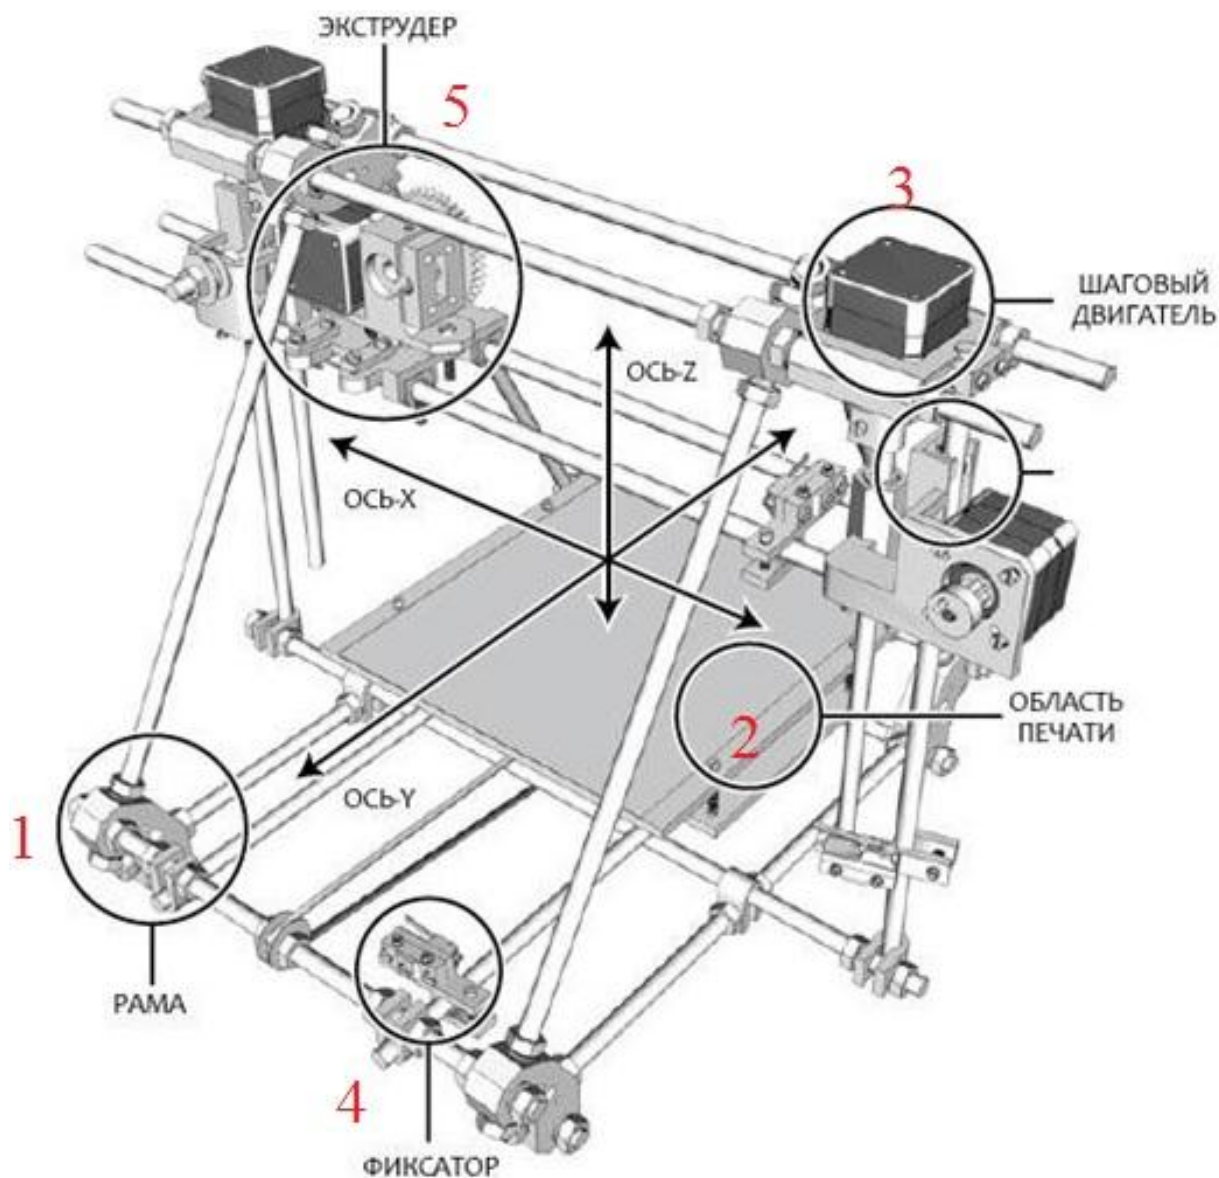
Устройство 3D принтера. 1 – рама (каркас); 2 – рабочая поверхность; 3 – шаговые двигатели; 4 – фиксатор (концевик); 5 – экструдер
